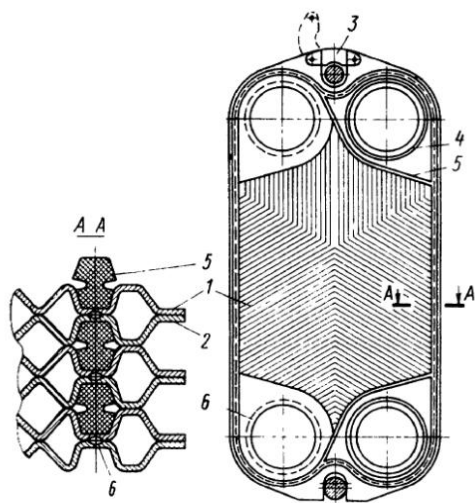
Конструкция попарно сваренных пластин полуразборного аппарата: 1 — правая пластина; 2 — левая пластина; 3 — подвеска; 4 — малая прокладка; 5 — большая прокладка; 6 — штриховая линия — линия контактного шва попарной сварки пластин
